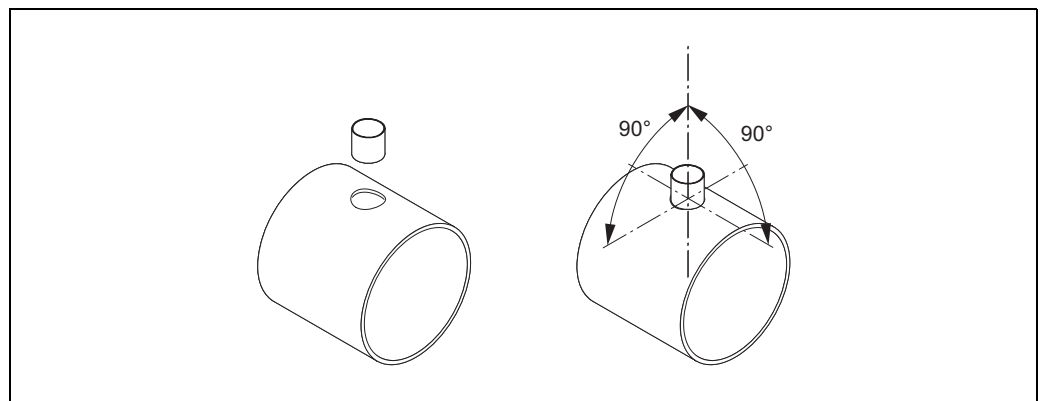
Positionierung des Schweißstutzens auf dem Rohr (oder Kanal)
